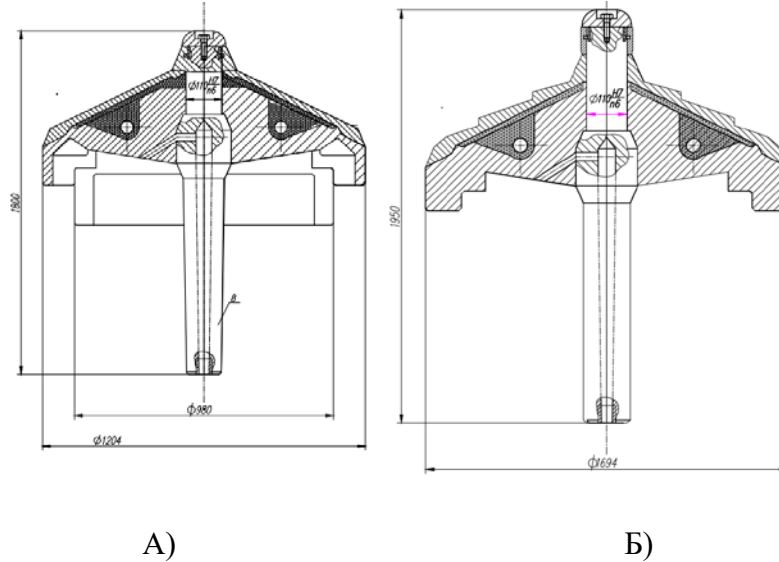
Креслення: А) Базового рухомого конуса; Б) Модернізованого конуса.
